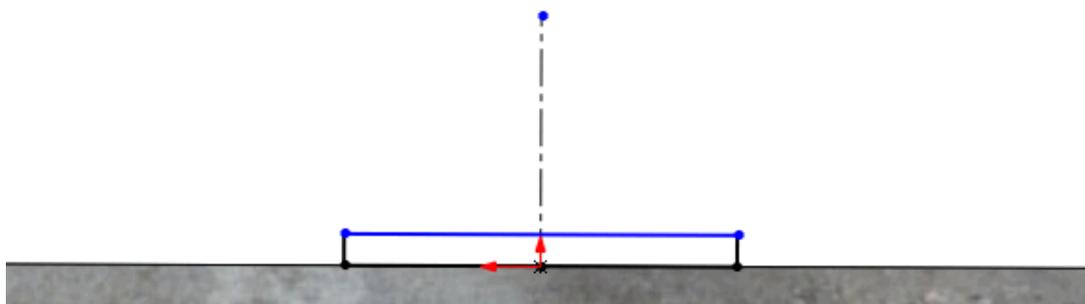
Adicionando linha de construção e outro retângulo ao esboço da bainha.
